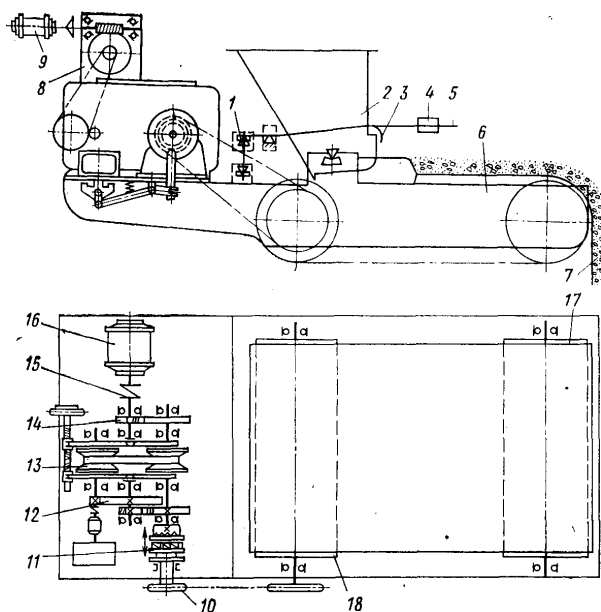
Весовой дозатор непрерывного действия с механической системой регулирования и его кинематическая схема.
